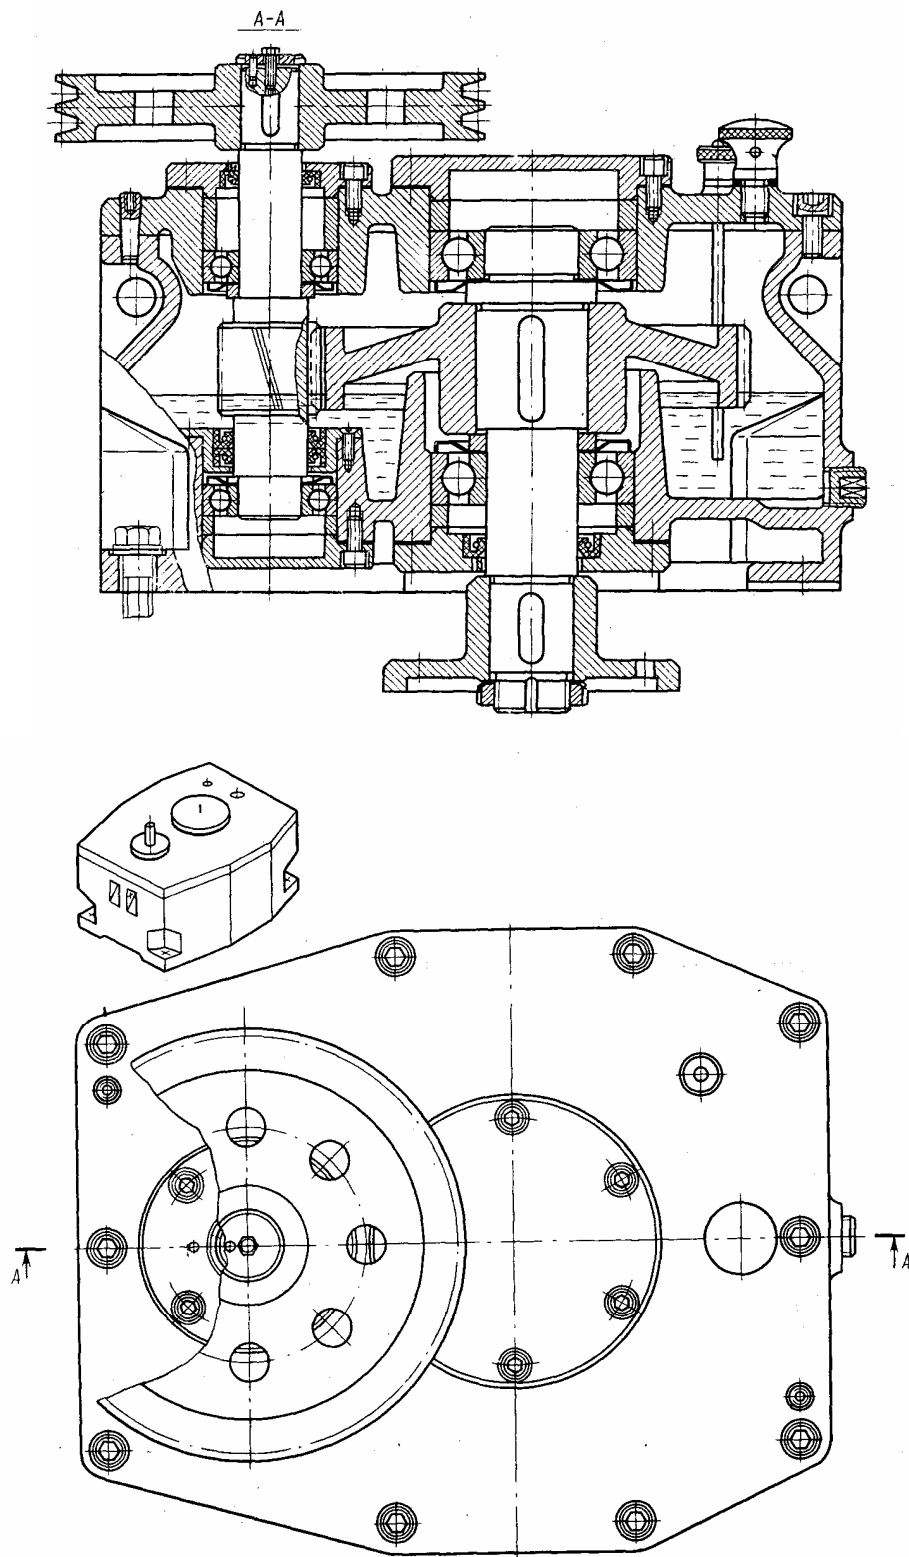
Редуктор (A13) цилиндрический одноступенчатый с вертикальными валами
